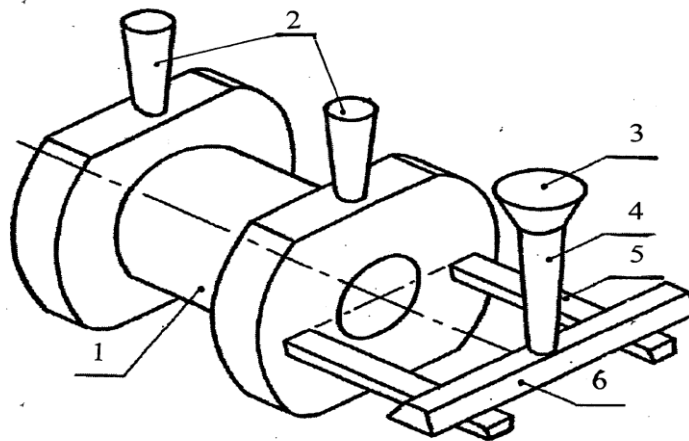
Эскиз отливки с элементами литниковой системы:
